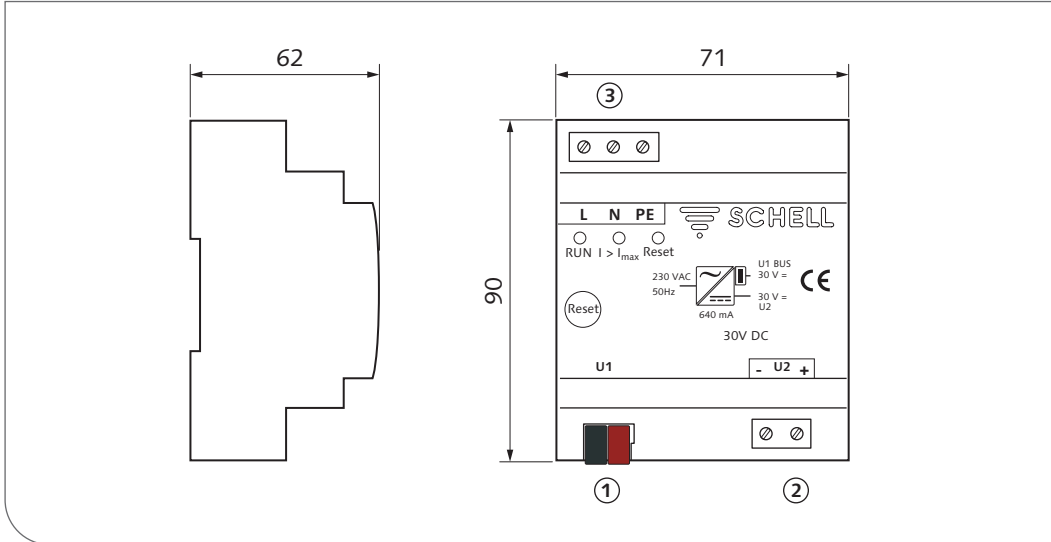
Adaptador de red de bus SWS de 30 V. Dimensiones
